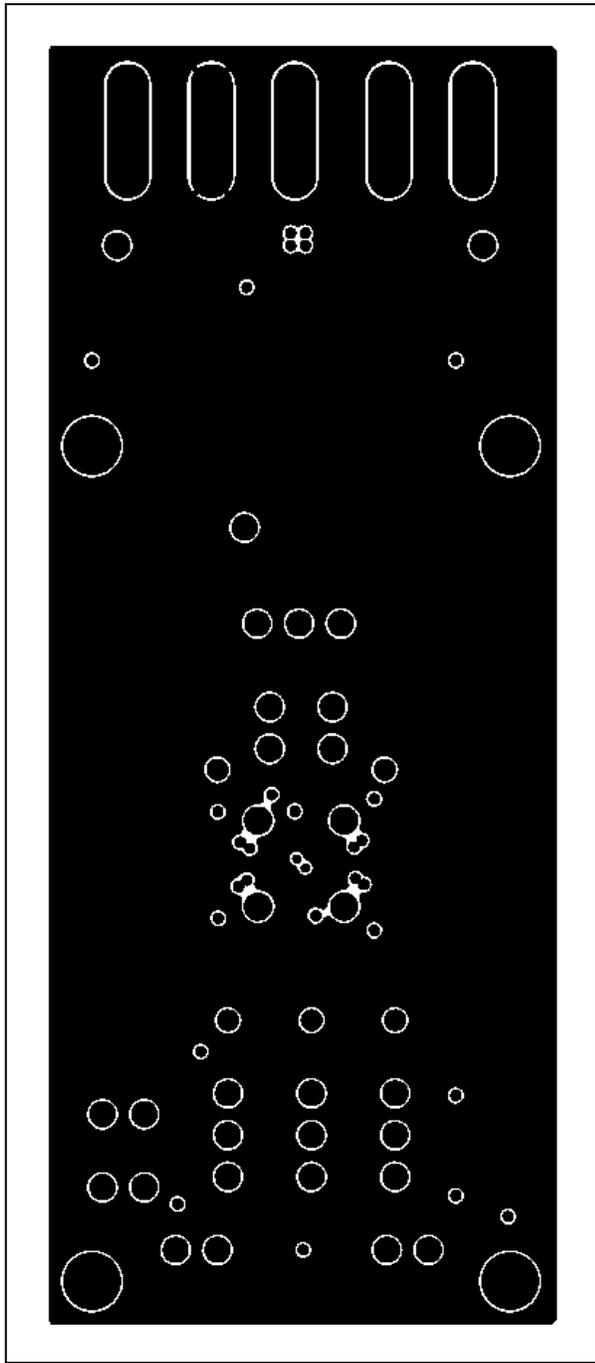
MAX3805 の PCB レイアウト—グランドプレーン
